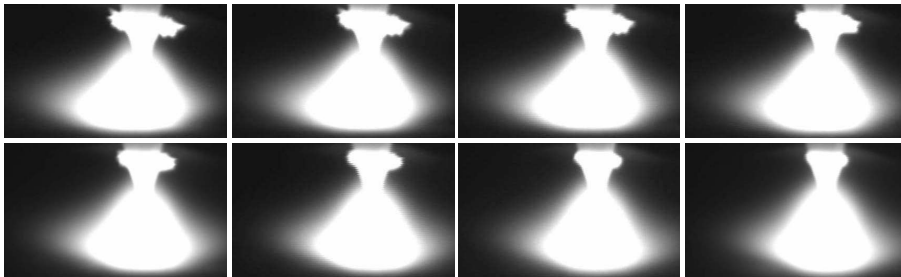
Vue de cote de l'arc électrique lors du soudage A-TIG respectivement pour  $x = 0; 1; 2; 3; 4; 5; 6; 7$  mm
